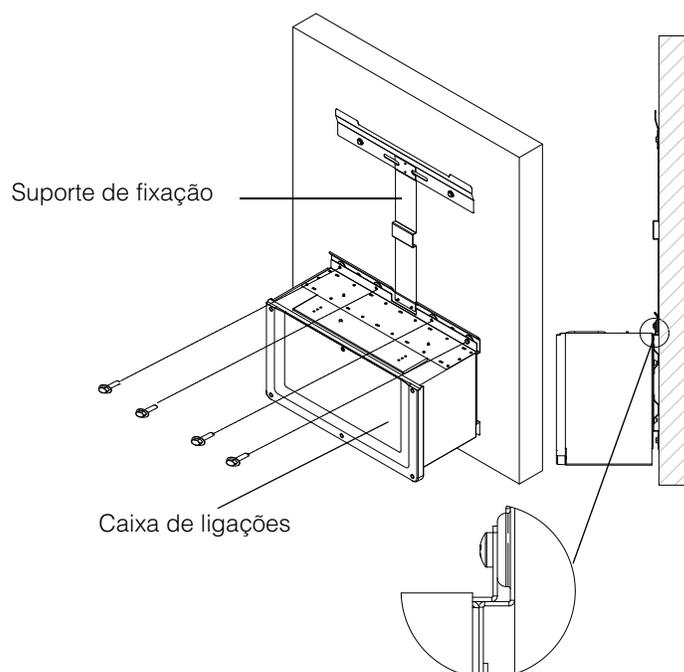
Fixação da caixa de ligações no suporte de fixação
